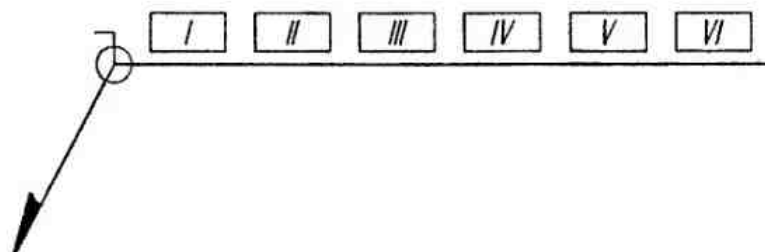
Полное условное обозначение сварного шва
